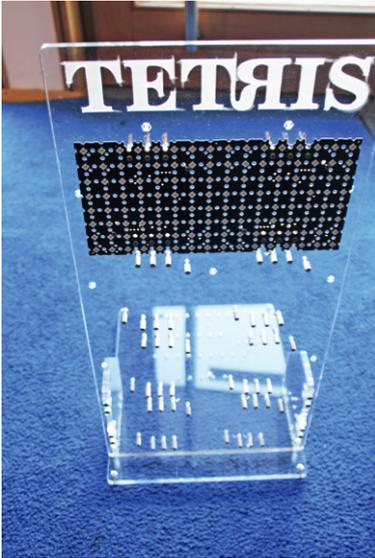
Der Lasercutter hat genau gearbeitet – die Panels passen perfekt!
